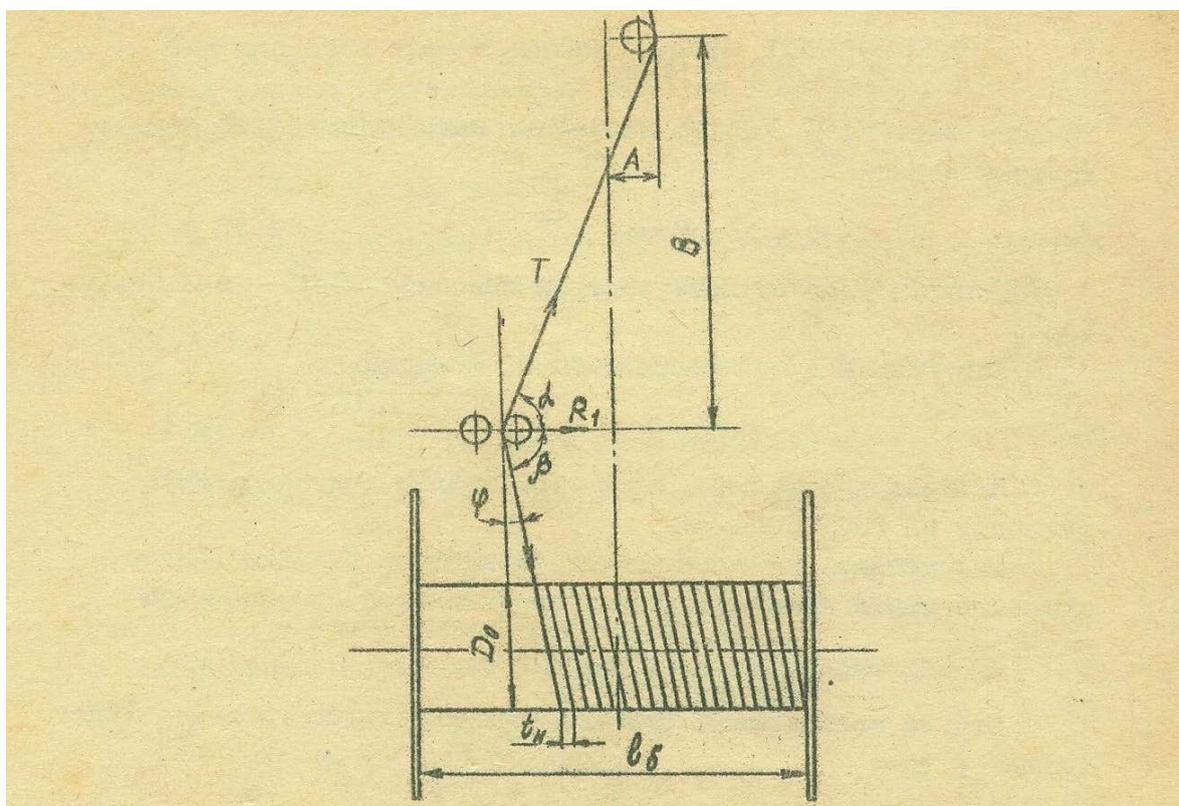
Схема проводки каната и его укладки на барабан лебедки
